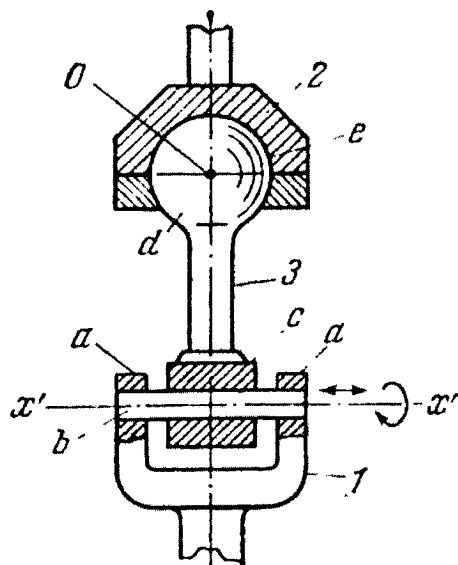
З'єднання з циліндричною напрямною: 1, 2, 3 – ланки, а – вушка ланки 1, б – циліндрична напрямна, с – втулка ланки 3, d – кульова головка ланки 3, e – кульова порожнина ланки 2
